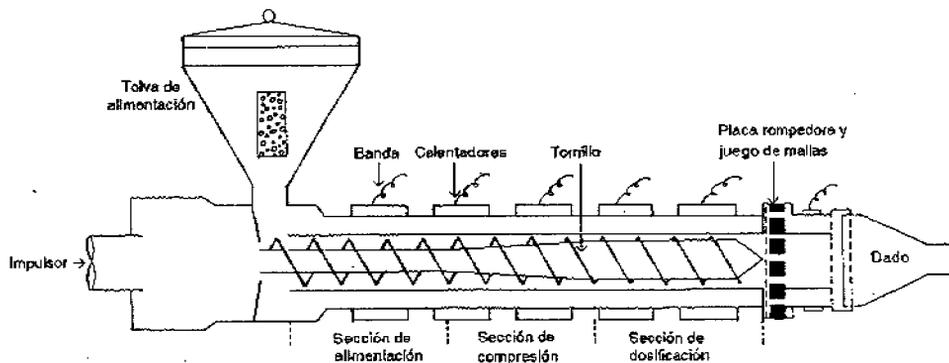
Características principales de un extrusor de tornillo sin fin simple
